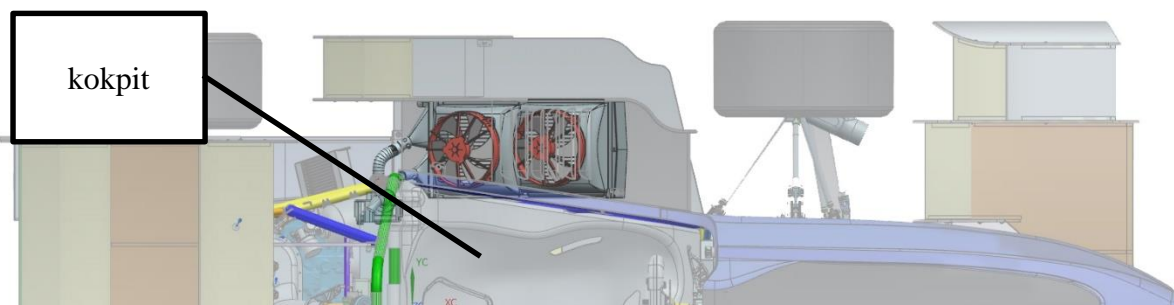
Umístění chladiče v zástavbovém prostoru formule
